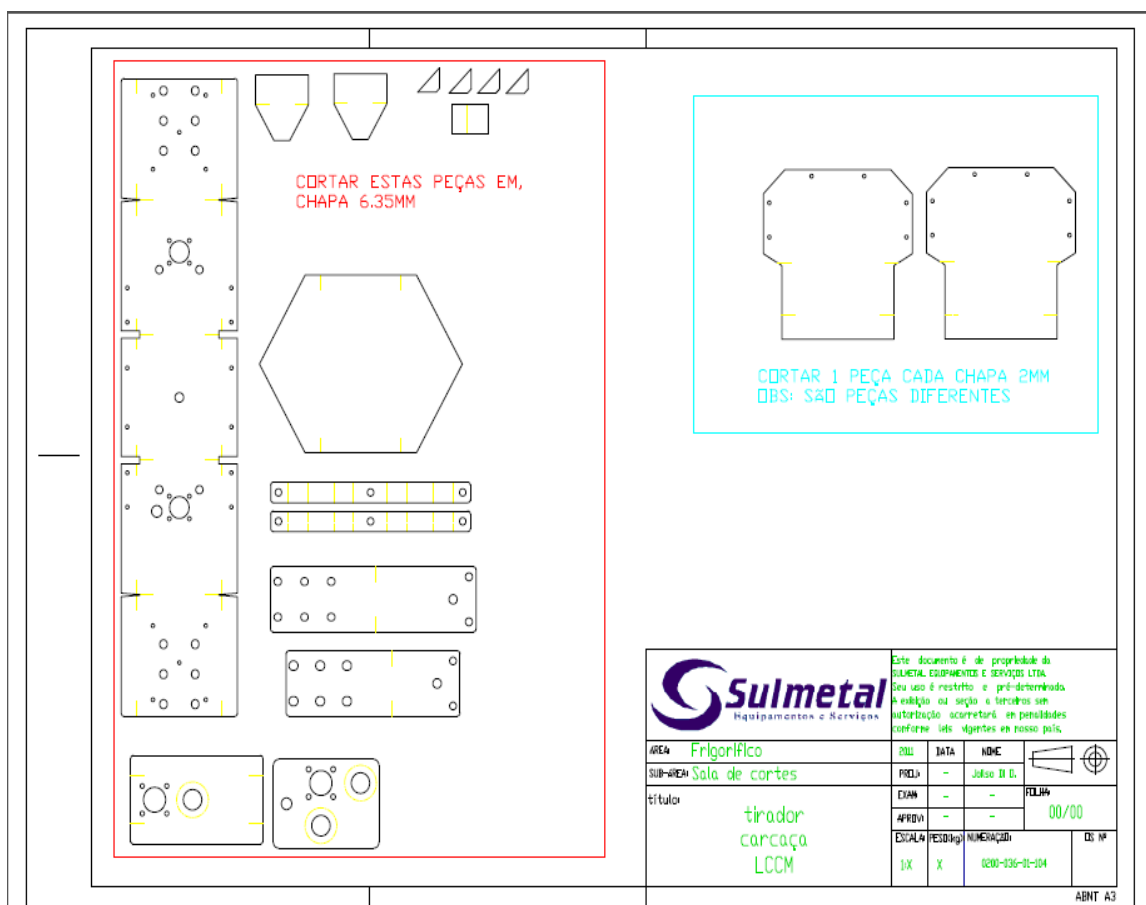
Projeto mecânico - Plano de corte jato d' água
